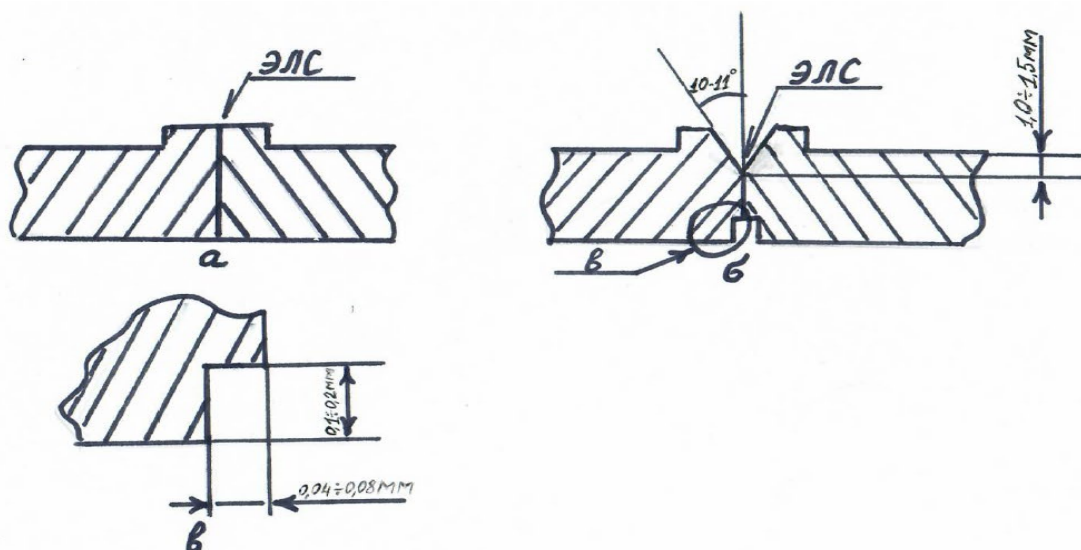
Схема конструкций стыкового соединения: а – классическое стыковое соединение; б, в – сварное соединение с измененной геометрией стыковых кромок
